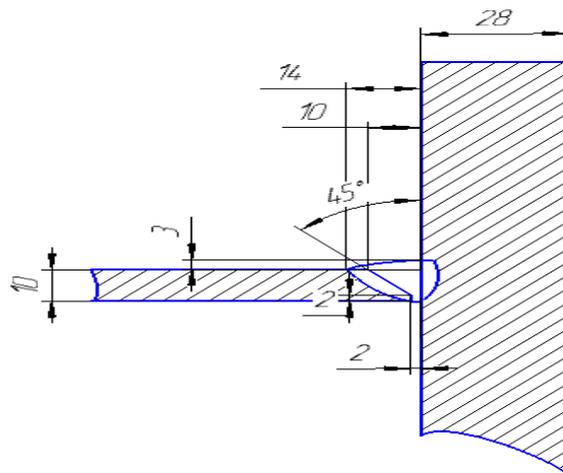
Эскиз сварного соединения по ГОСТ 14771–76 Т6
